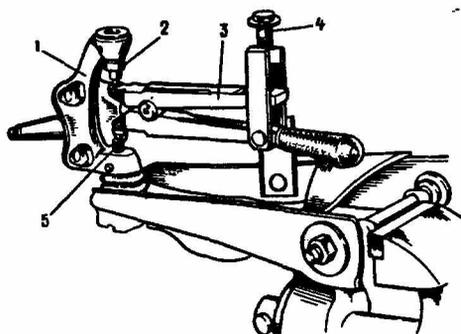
Отсоединение нижнего рычага: 1 - поворотный кулак; 2 - упор; 3 - приспособление 67.7801.9513; 4 - болт; 5 - палец шарового шарнира
